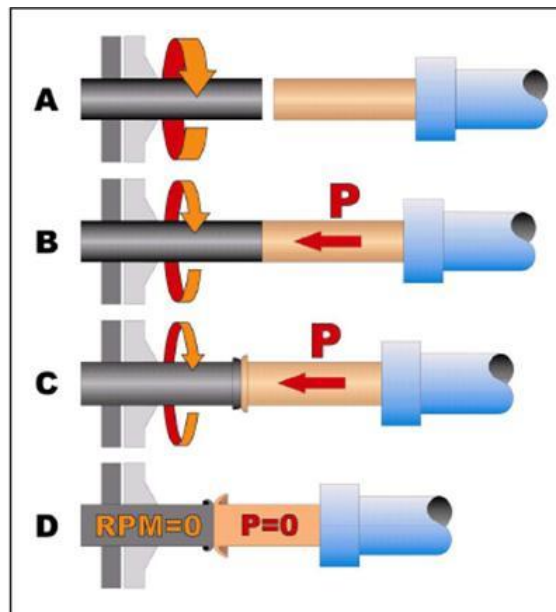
Esquema de sequência básica da Soldagem por Fricção Inercial
